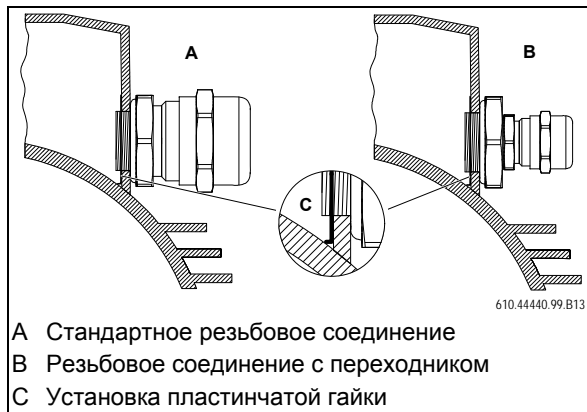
Резьбовые соединения с пластинчатой гайкой
